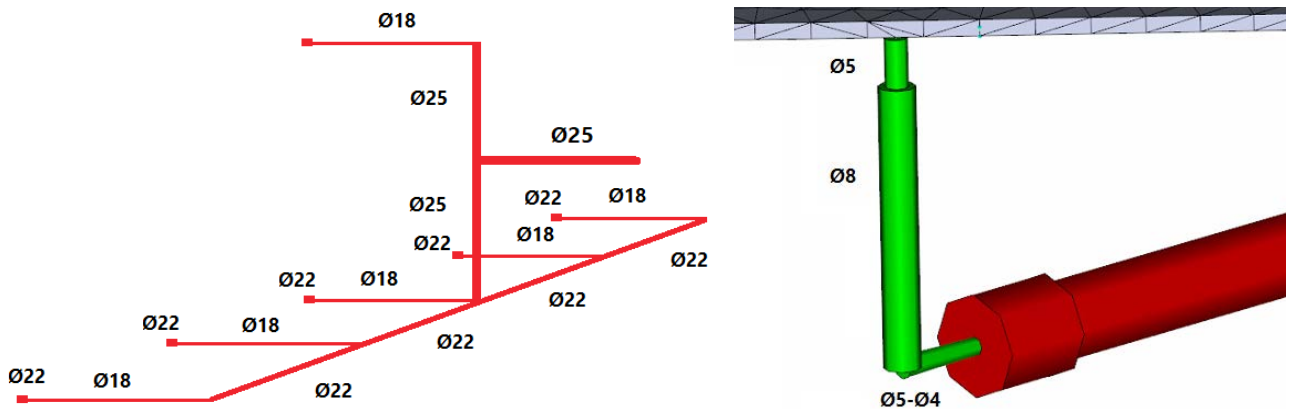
Esquema canal caliente y detalle de la forma modelada para el tramo frío hasta la pieza
